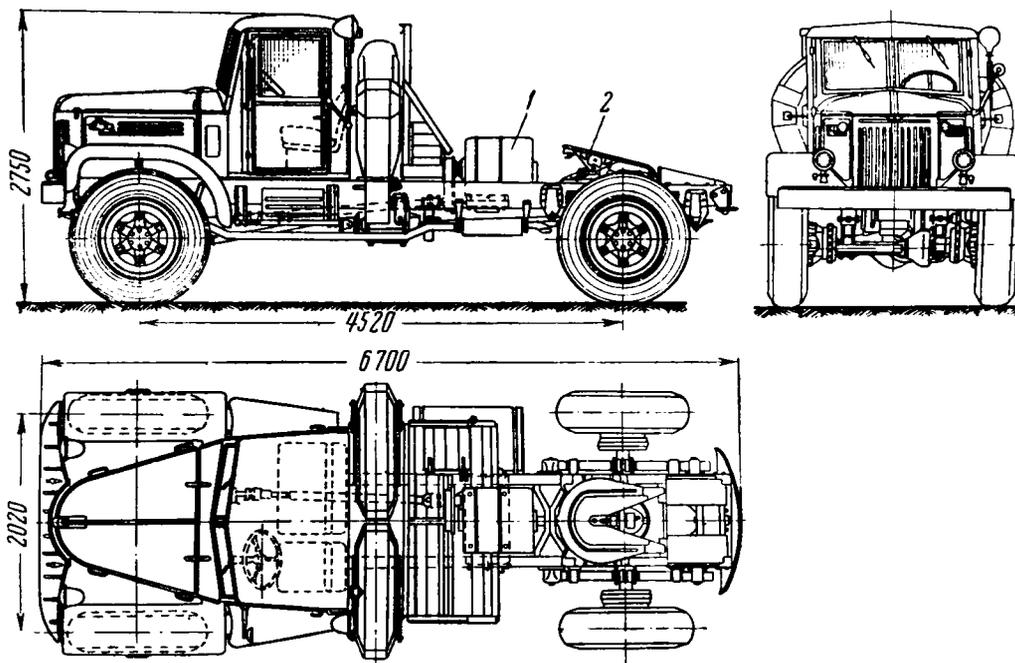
Лесовозный тягач на базе автомобиля МАЗ-501 для работы с активными прицепами
